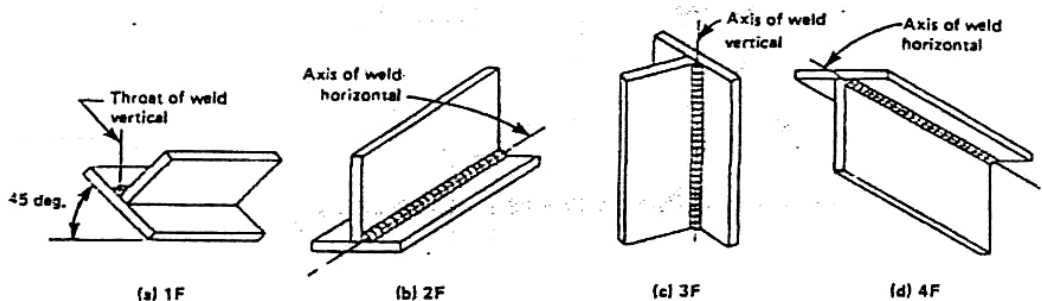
Posiciones de Soldadura en placas son soldadura de filete
